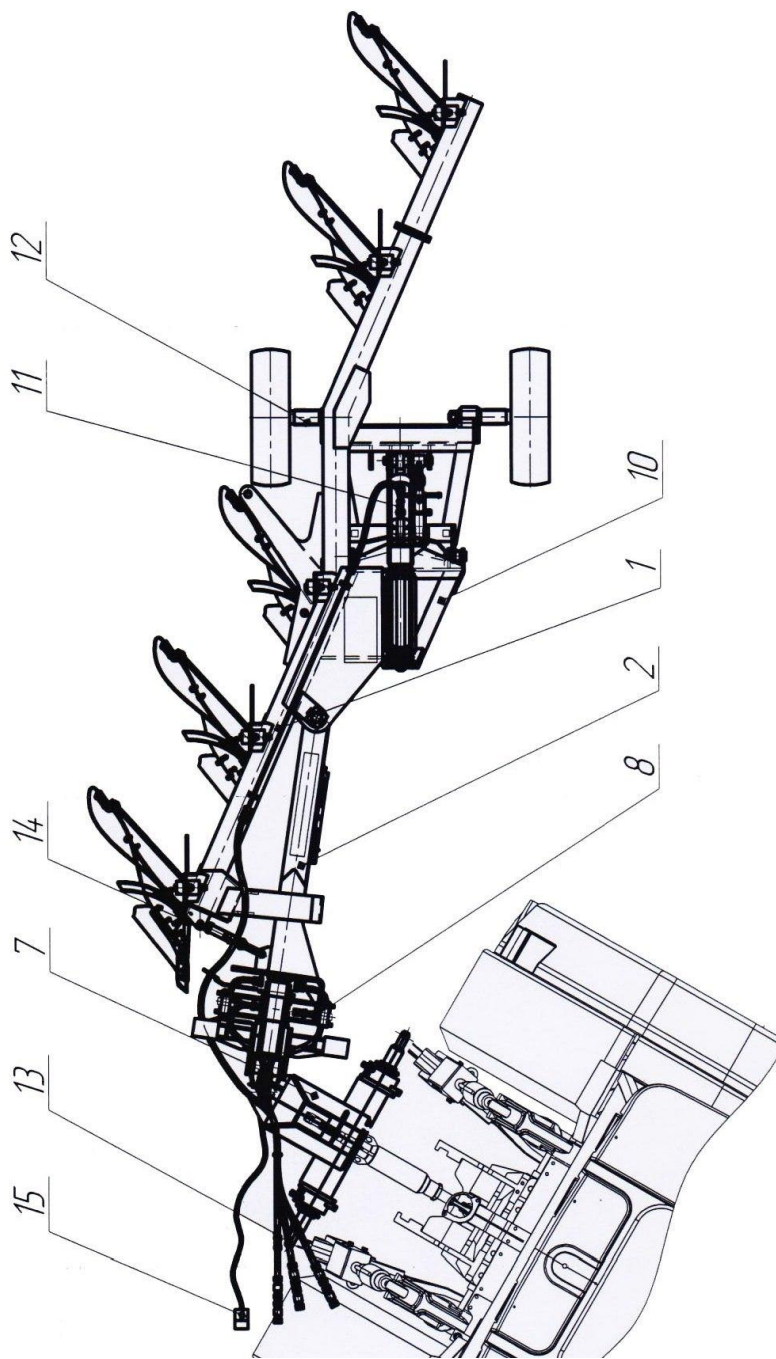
Плуг ПО-4+1 (вид сверху)
